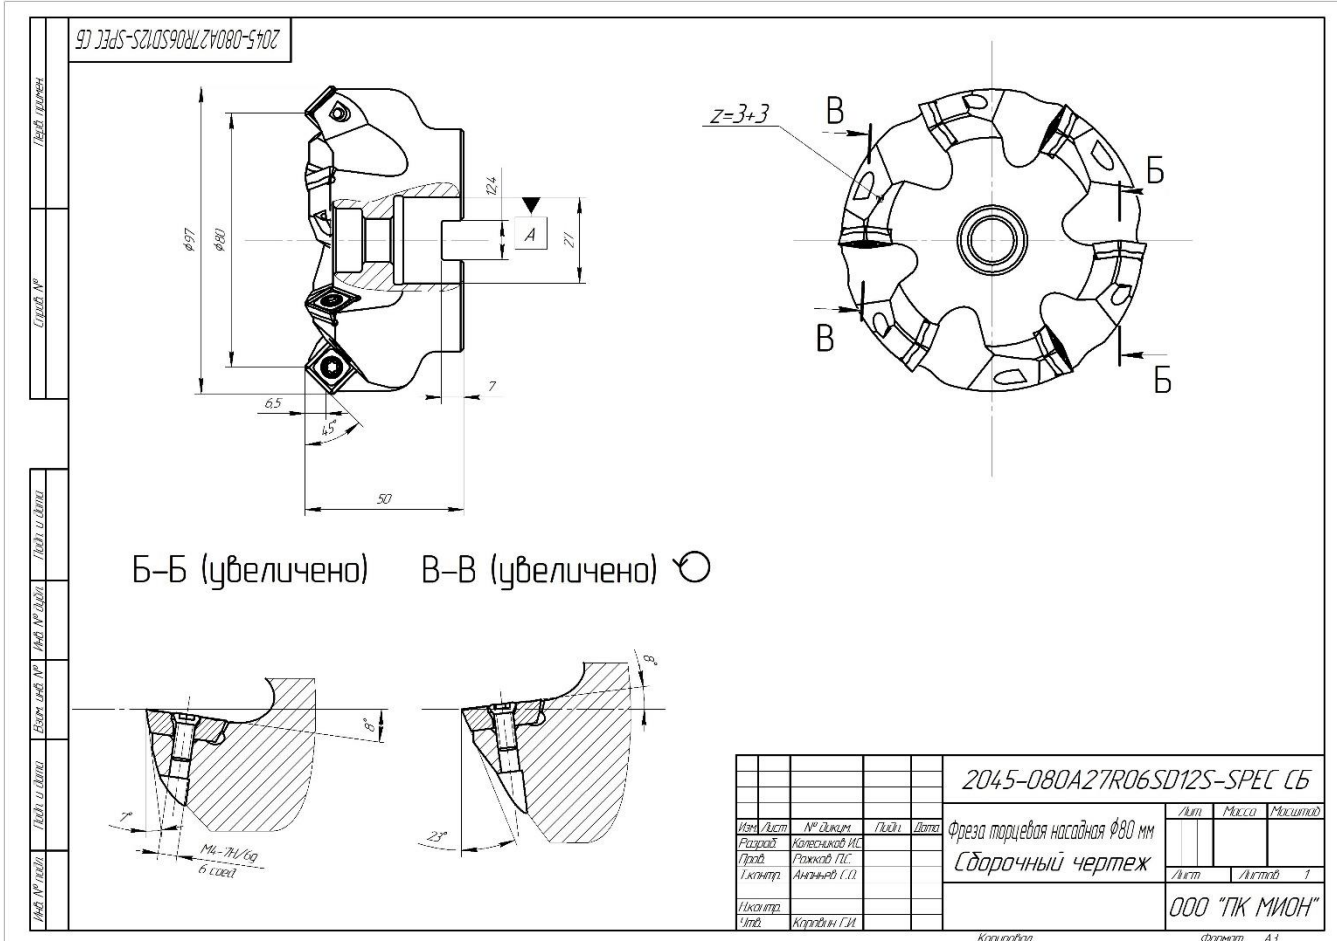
Сборочный чертёж торцевой фрезы
